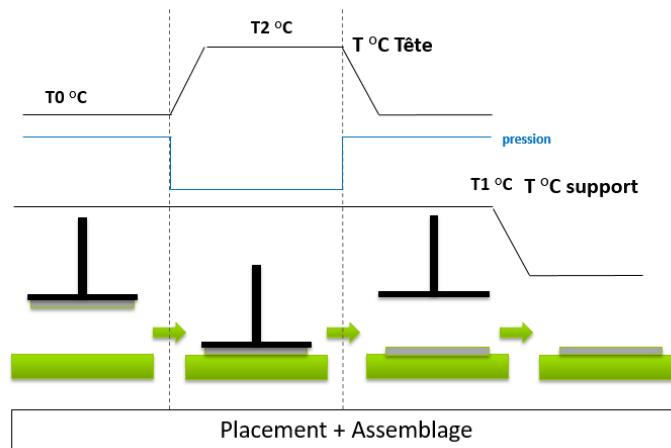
Schéma du procédé d'assemblage par thermocompression.
